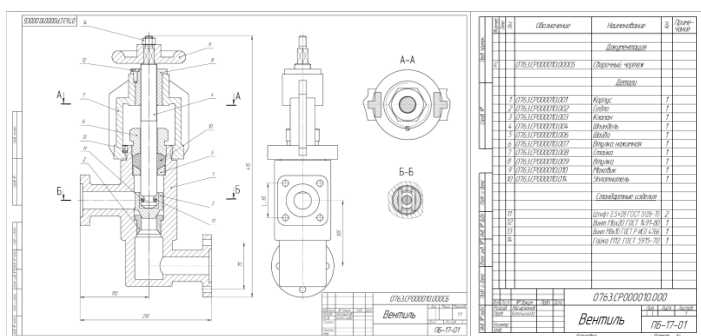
Сборочный чертеж и спецификация вентиль
